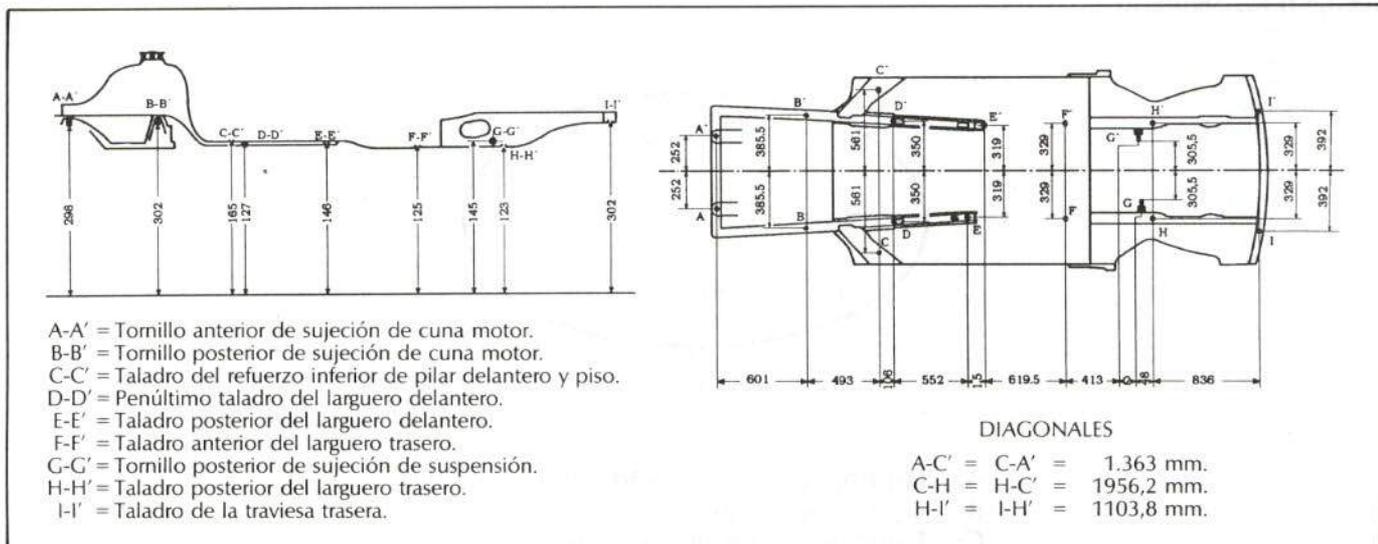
Dimensiones del vehículo en planta y alzado.
